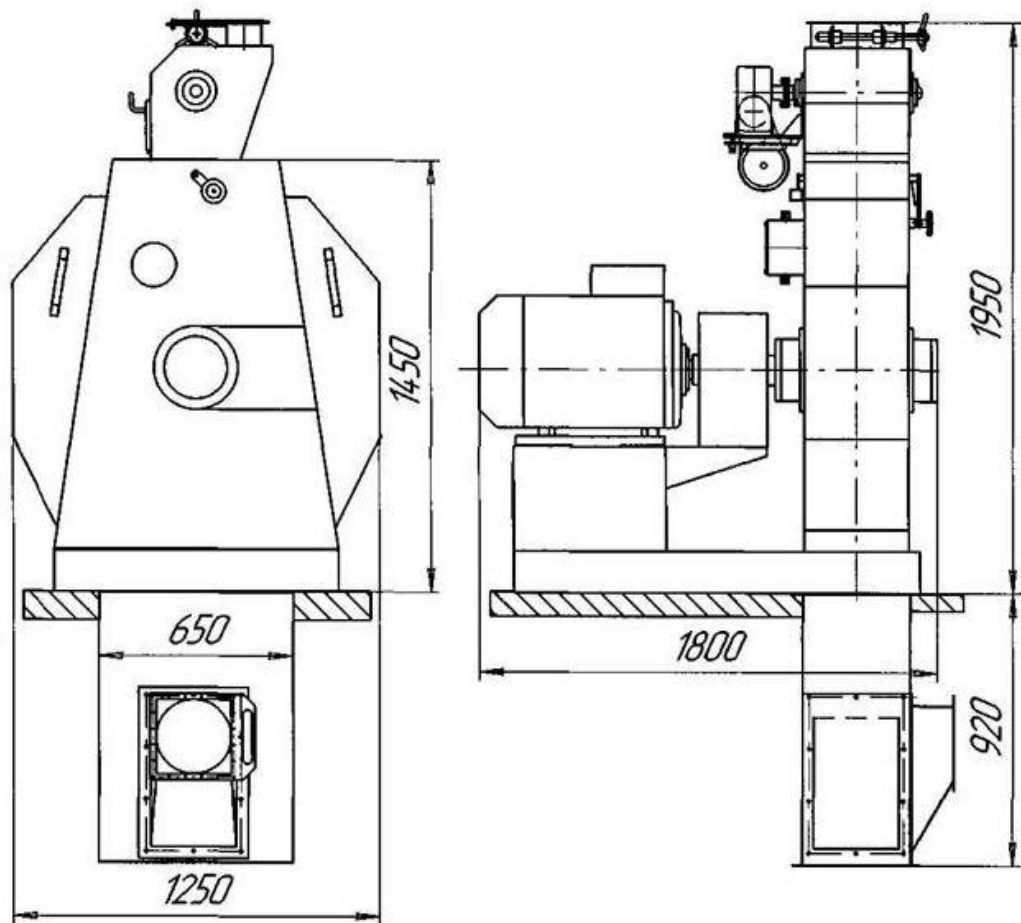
Загальний вигляд зернової молоткової дробарки марки ДКМ.
